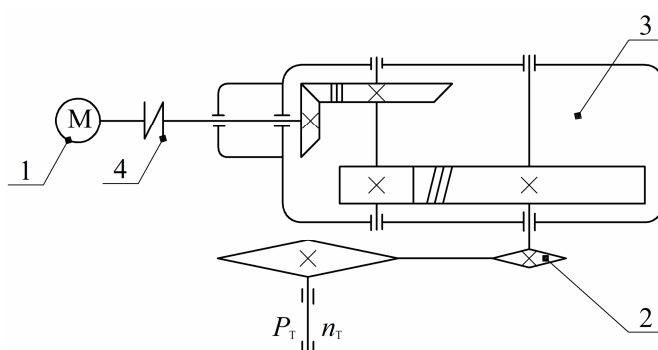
Кинематическая схема привода навозоуборочного транспортера
